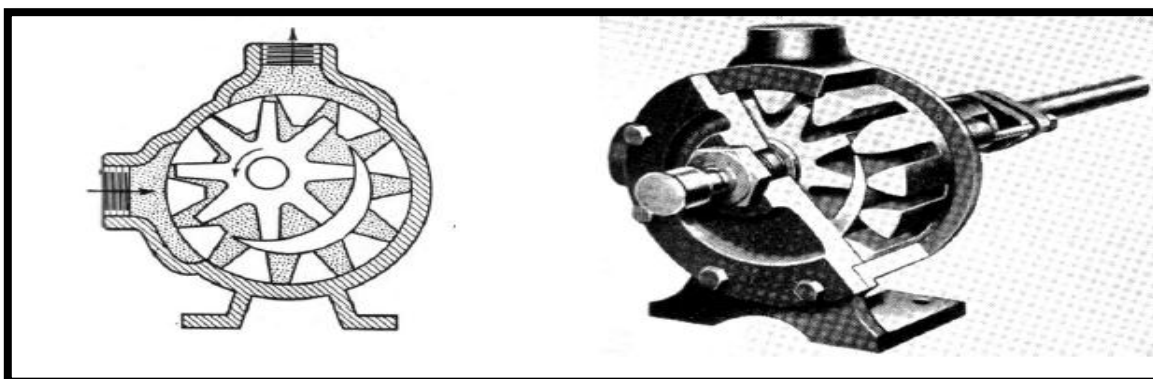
Bomba de engranajes exteriores, rígidos
